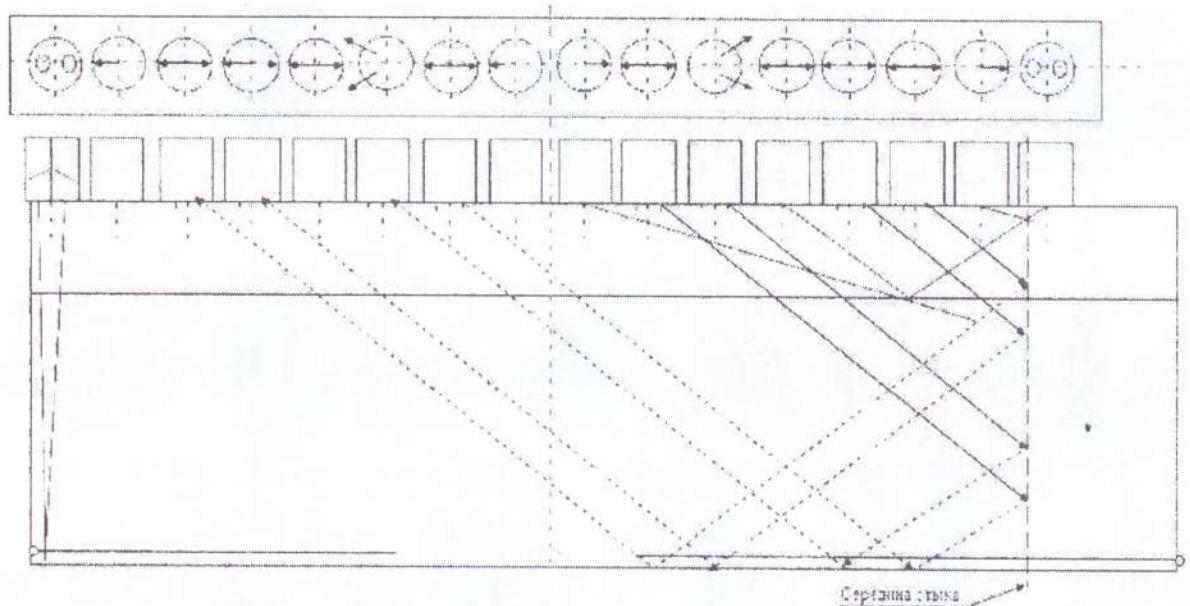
Схема прозвучивания стыка блоком резонаторов №1
